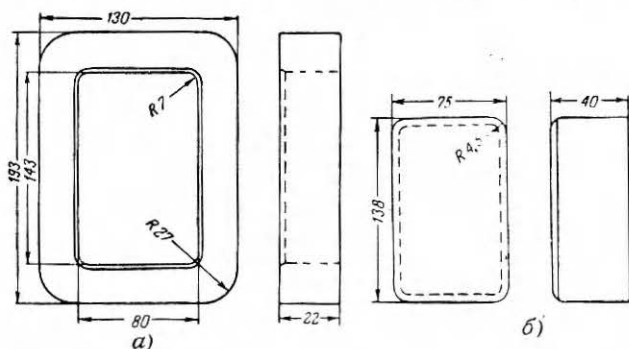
Чертеж приспособления для изготовления футляра приемника.
